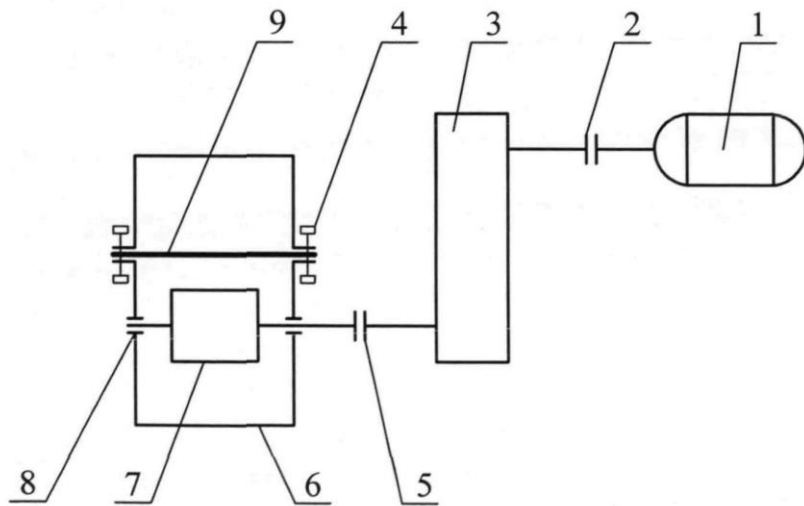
Кінематична схема одновалкової дробарки
